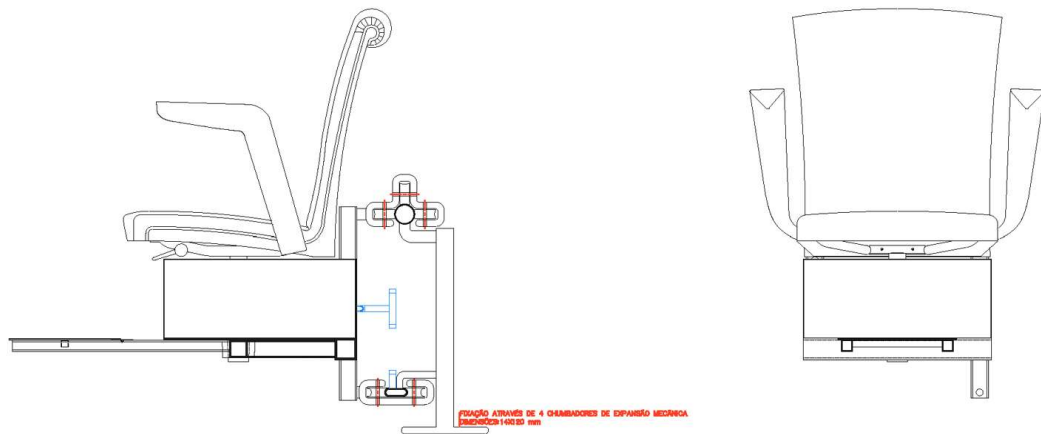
Projeto detalhado da estrutura da cadeira elevatória
